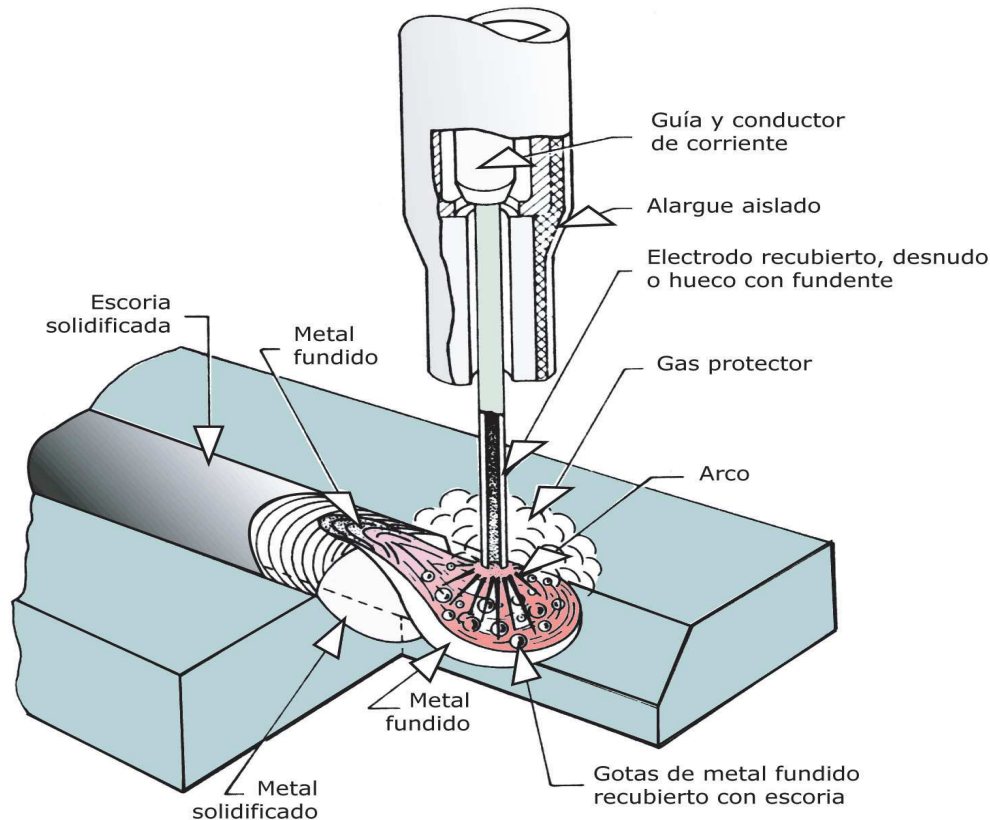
Ilustración del proceso de fusión en la soldadura GMAW
